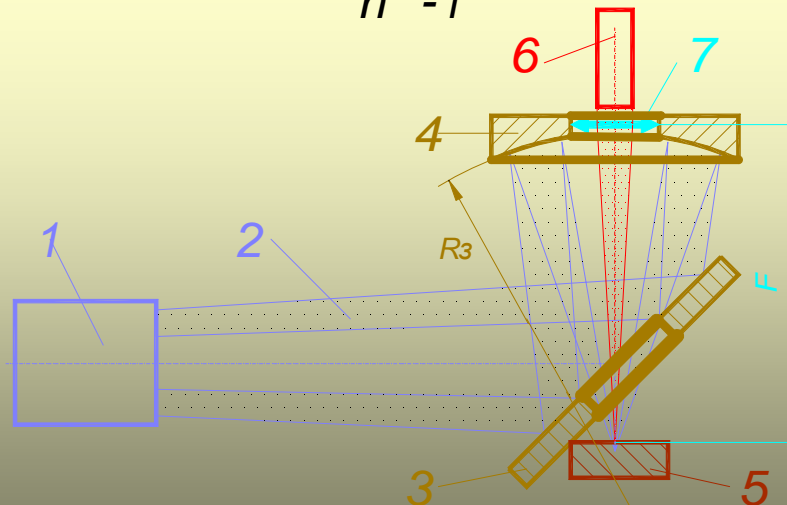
(9.6). Схема ЛТУ з пристроєм для позиціювання заготовки в каустиці пучка випромінювання, перетвореного ОПС з дзеркальними елементами
